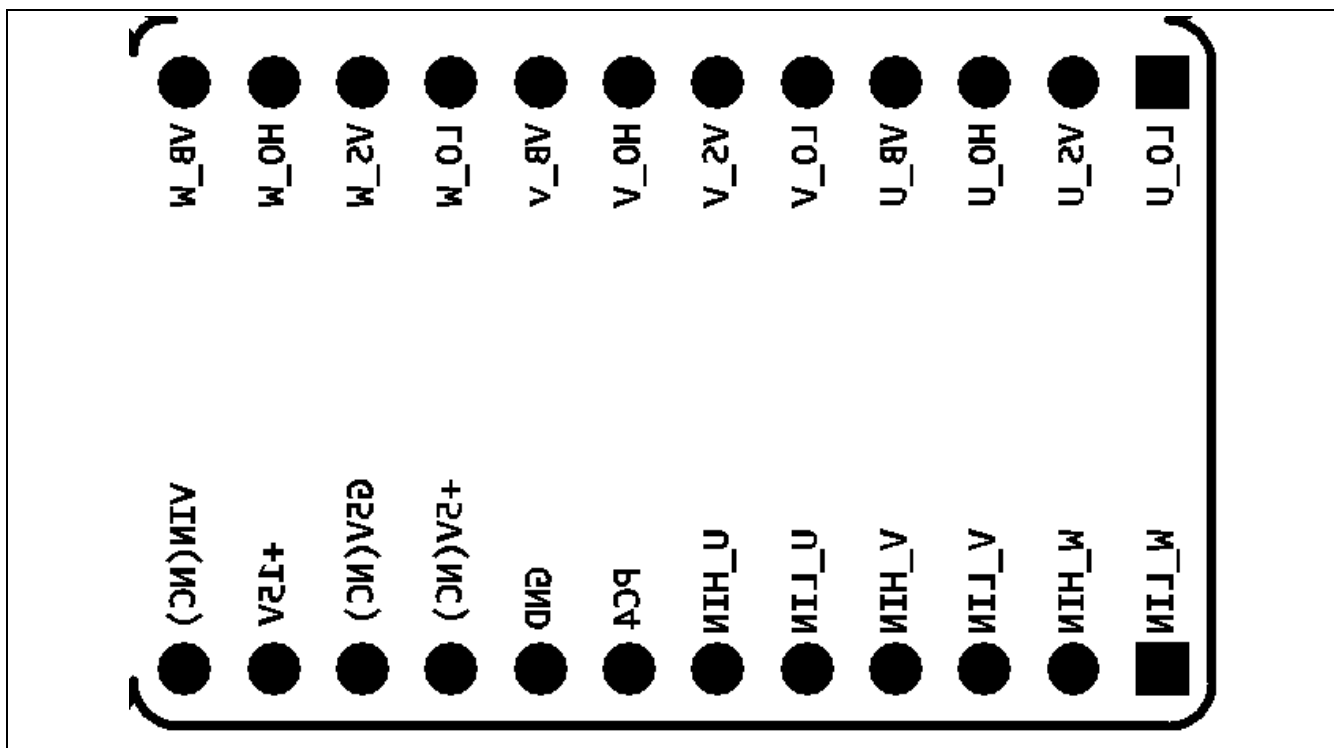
Gate Driver IR2101PCB 佈局-反面
